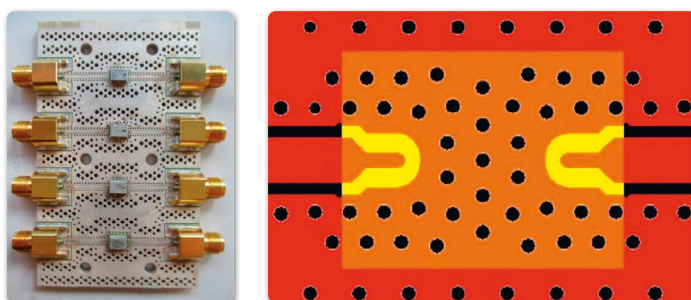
Testplatinen- und PCB-Layout der Kundenmessung von BFHKI-Filtern
